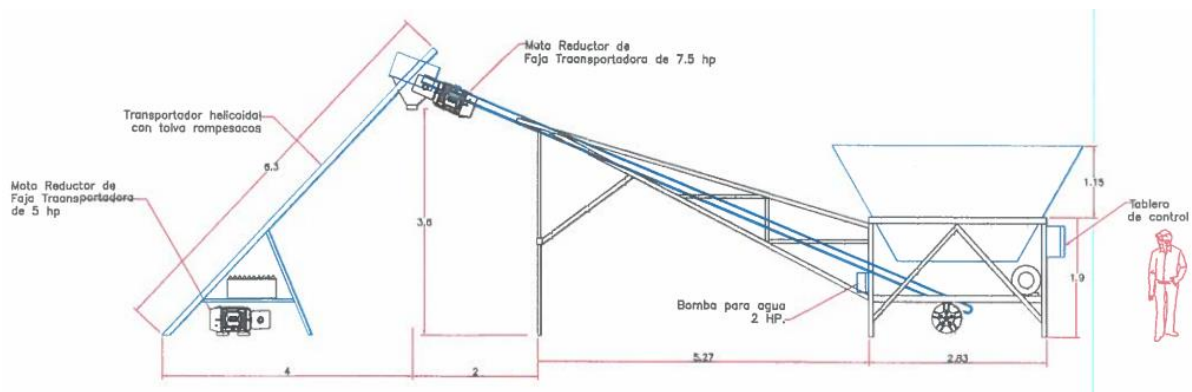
Esquema de planta dosificadora. Tomado de “Planta dosificadora de 24m3/hora”, por Auto Hormigoneras del Perú SAC., 2016.
